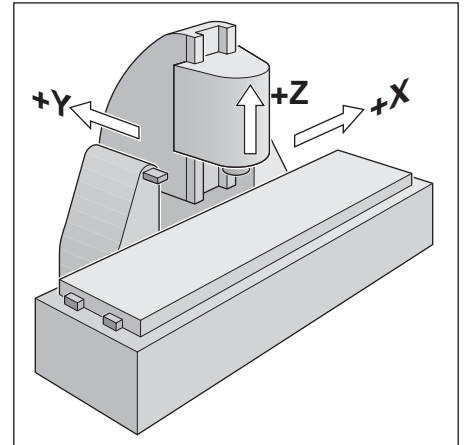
Déplacement de l'outil en Y et Z; déplacement de la table de la machine en X
